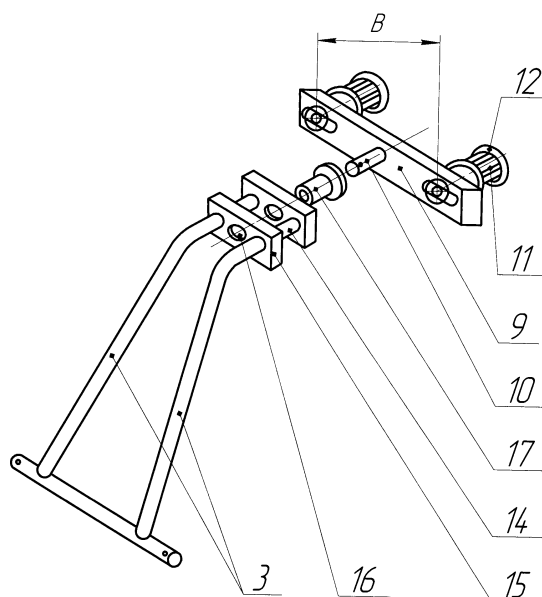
Штанга с приспособлением в аксонометрии (вид слева)
